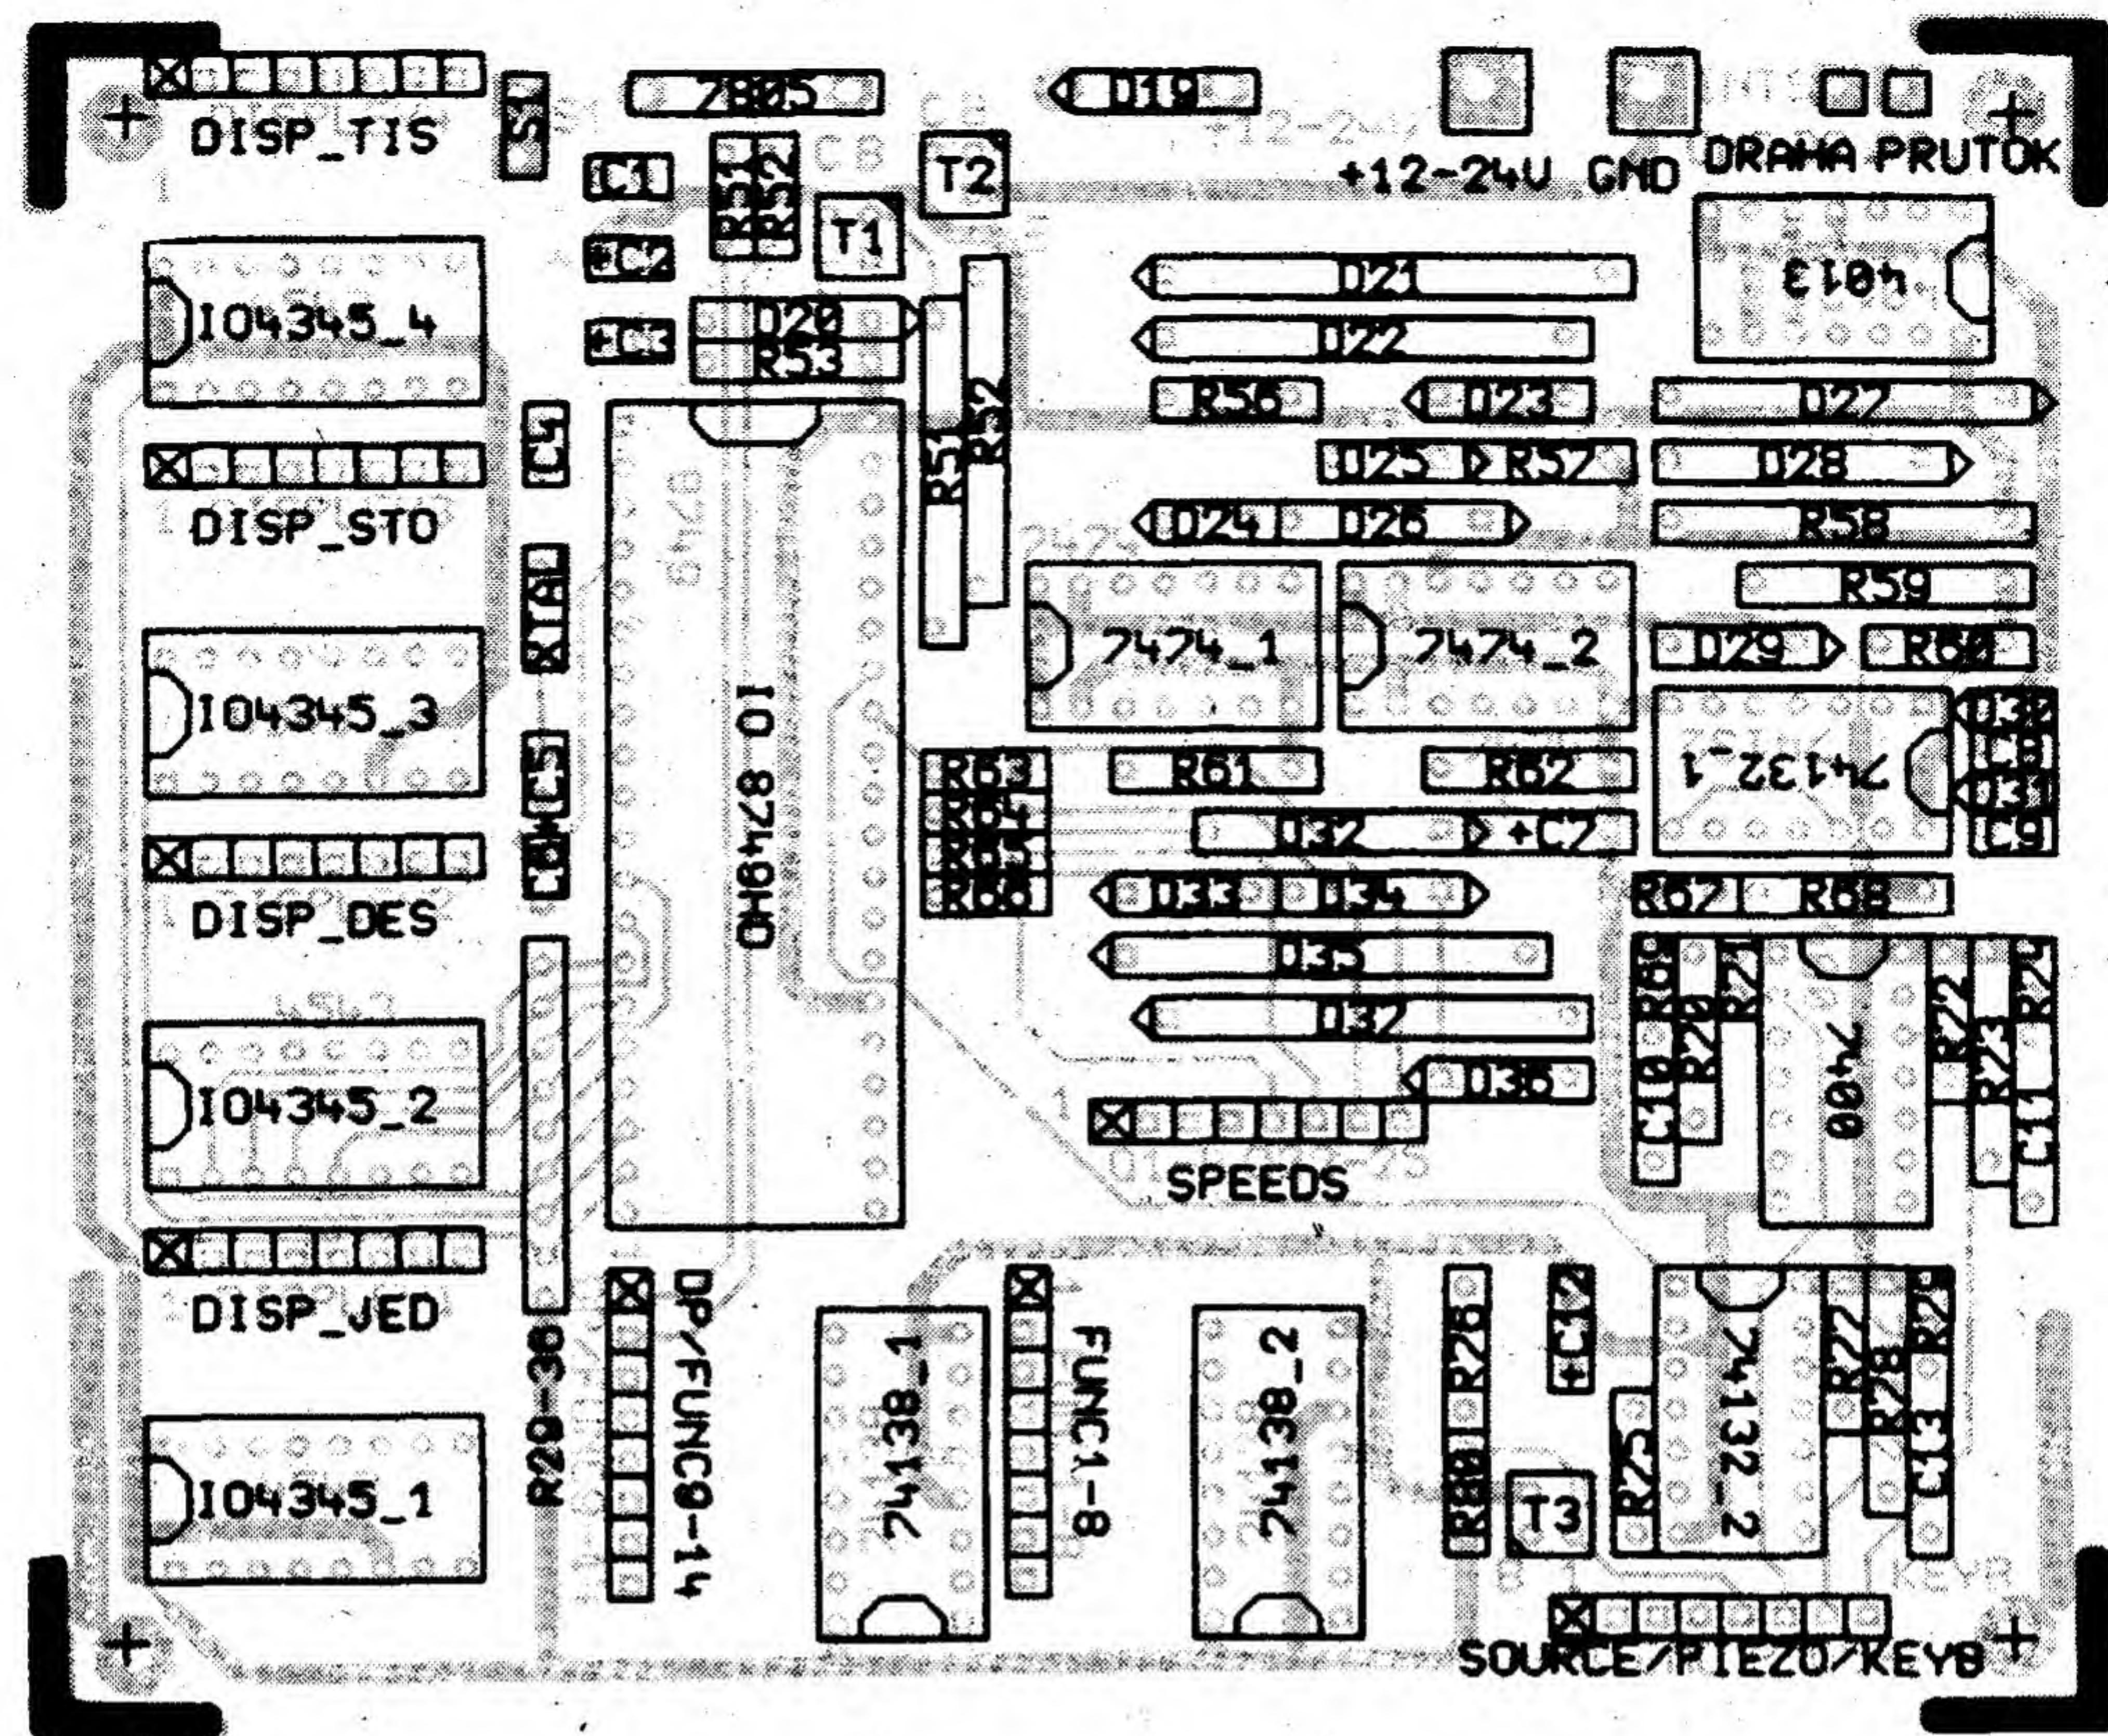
Rozložení součástek na jednostranném spoji základní desky
